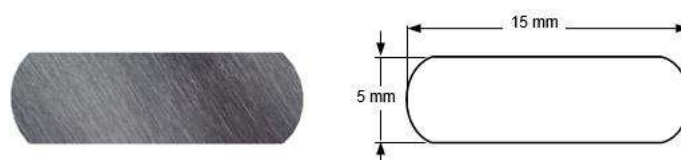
Exemplo da seção transversal de um arame da armadura de tração.
